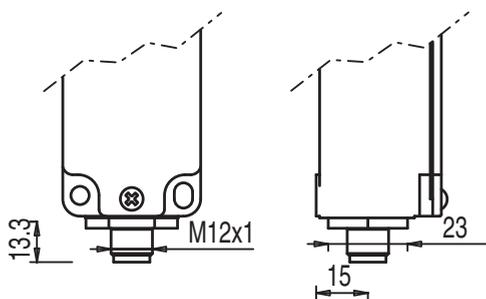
Dimensiones del S200-M4C1-M12 en mm (aquí dimensiones del conector M12)
